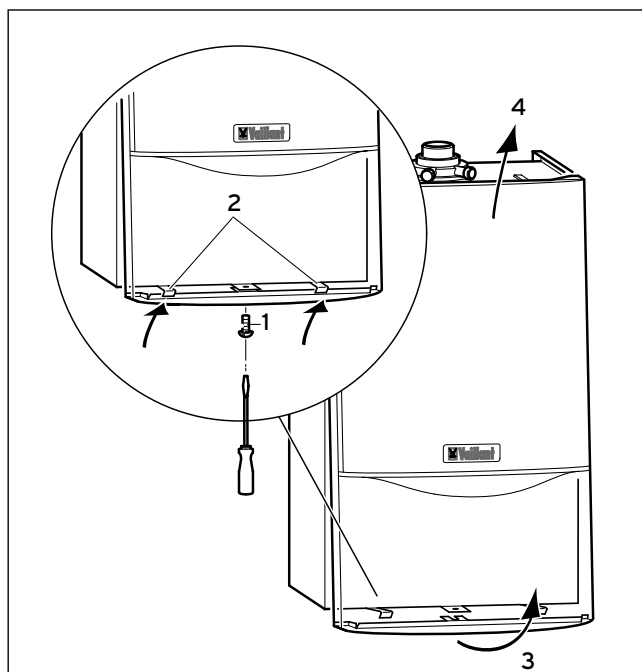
Rimozione/rimontaggio del pannello frontale degli apparecchi
